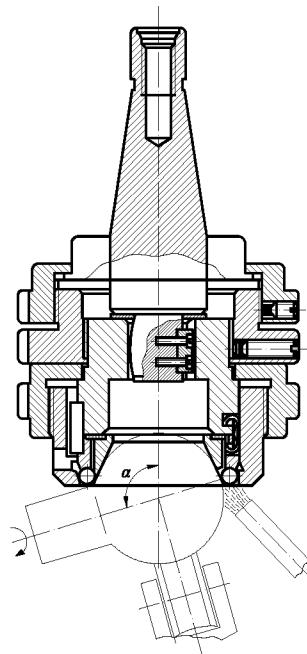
Планетарна головка для обробки сферичної поверхні
